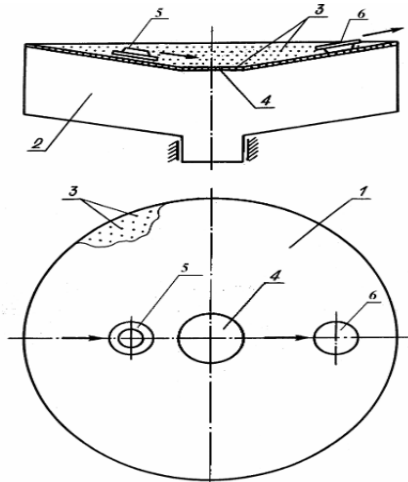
Схема работы пневматического устройства с газовой несущей прослойкой: 1 - рабочая поверхность; 2 - пневмокамера; 3 - газоподводящие отверстия (перфорация); 4 - позиция для базирования изделий; 5,6 - изделия
